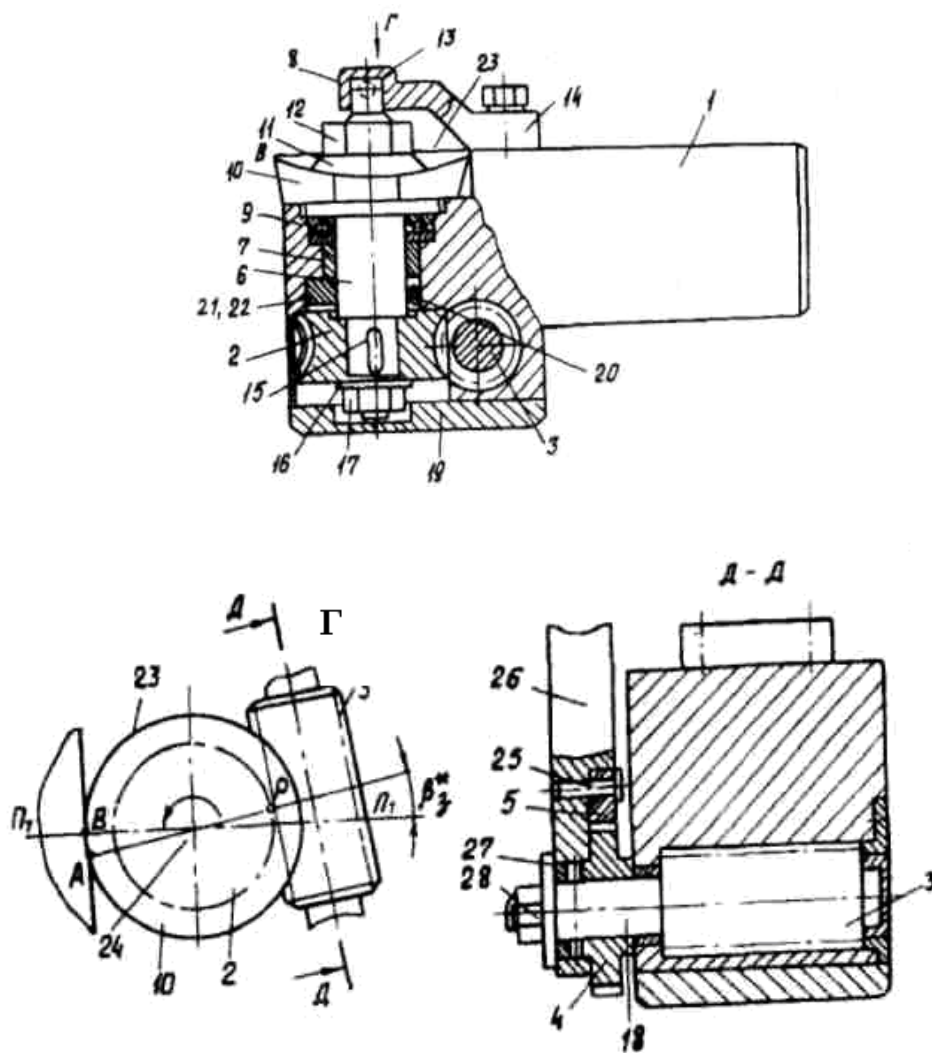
Эскиз шагового резца с червячным редуктором и храповым поворотным механизмом
